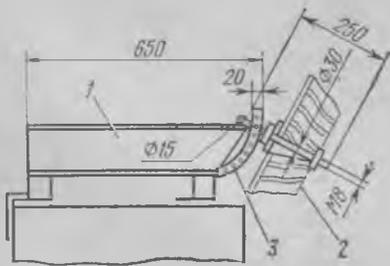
Приспособление для наплавки лопатки крыльчатки нагнетателя II ступени: 1 — швеллер 14 (основание); 2 — крыльчатка; 3 — фиксатор
